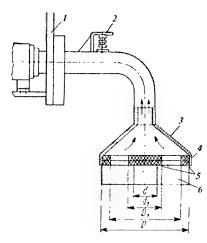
Вакуум-съемник: 1— вентилятор высокого давления; 2— воздушный клапан с электромагнитом; 3 колокол; 4— нижняя решетчатая плита; 5— резиновое уплотияющее кольцо; 6— выгалкиваемый абразивный круг
